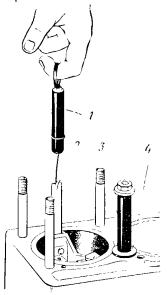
Подбор поршней к цилиндрам: 1 — динамометр: 2 — лентанцуп; 3 — втулка; 4 — пайба
